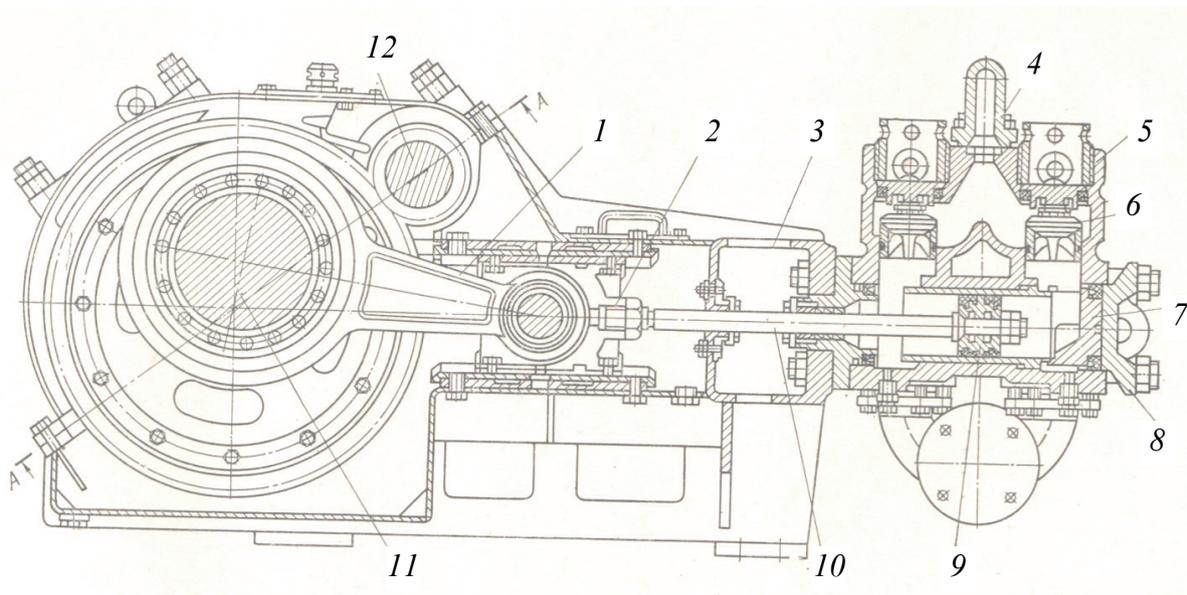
Насос 11Т: 1 – шатун; 2 – крейцкопф; 3 – станина; 4 – коллектор; 5 – клапанная коробка; 6 – клапан; 7 – нажимная коробка; 8 – цилиндрическая крышка; 9 – поршень; 10 – шток; 11 – коренной вал; 12 – трансмиссионный вал
